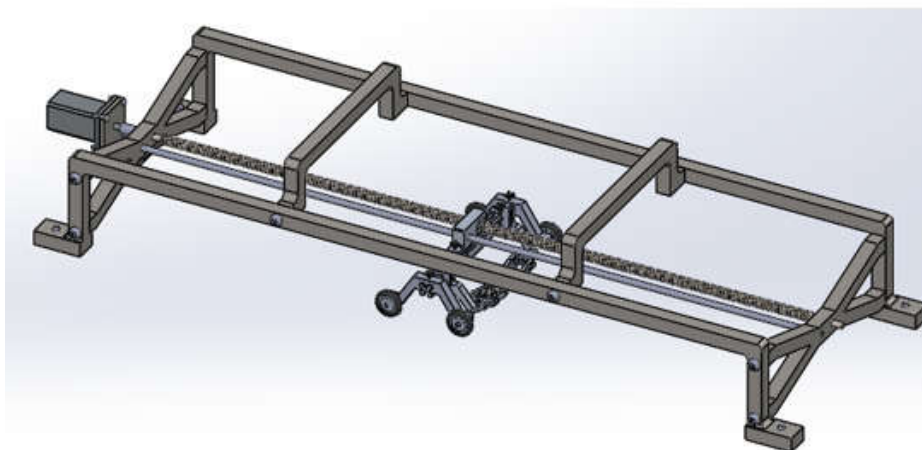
Модель конструкции сканера для перемещения датчиков вдоль сварного шва резервуара
